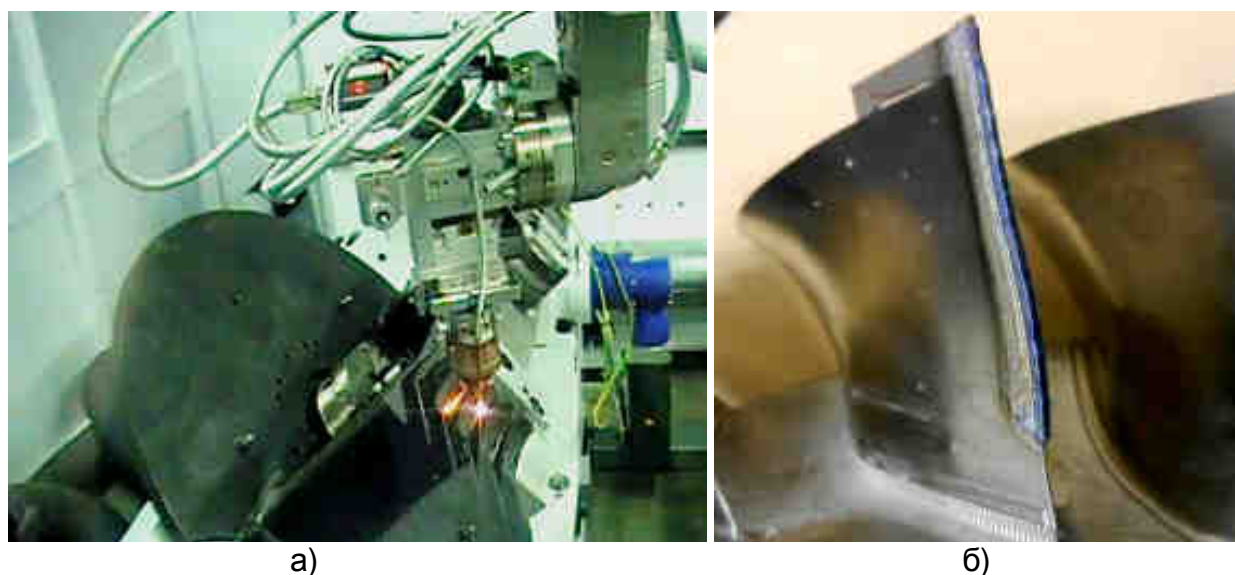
Процесс восстановления входной кромки лопатки (а) и наплавленная входная кромка лопатки (б) сектора моноколеса [8]
